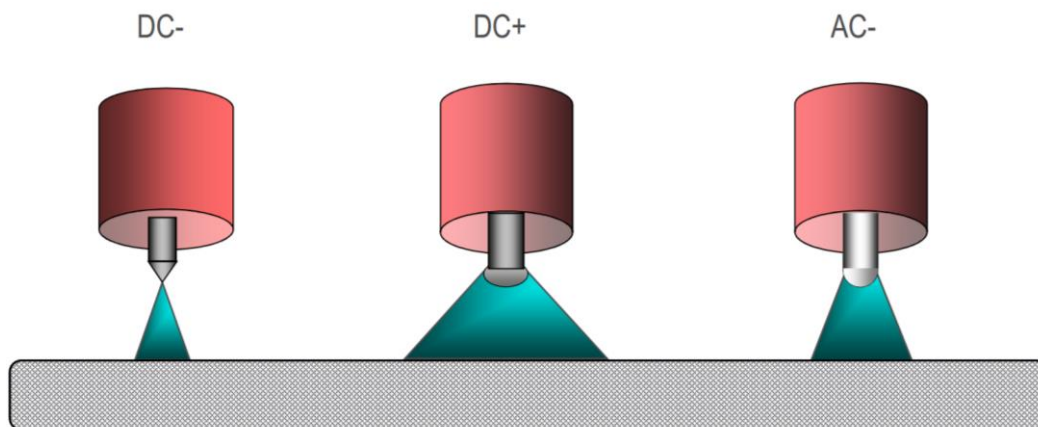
Вплив полярності зварювання на форму дуги
